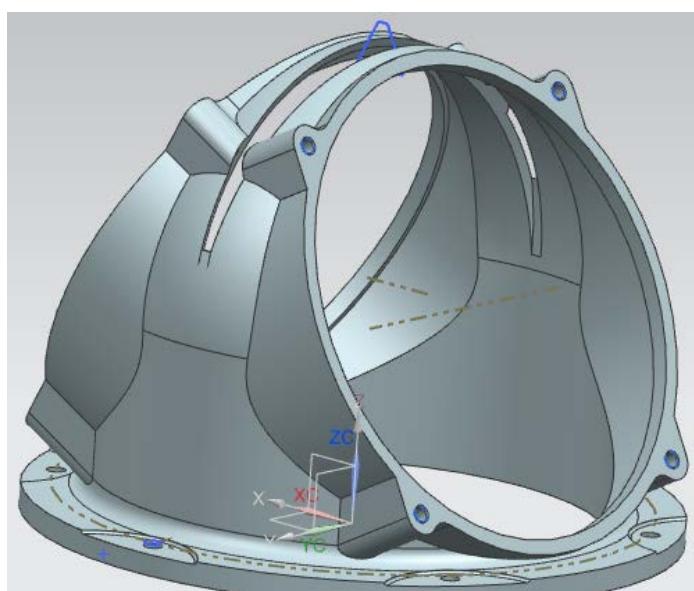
3D модель корпуса с вырезом под построение косынки
